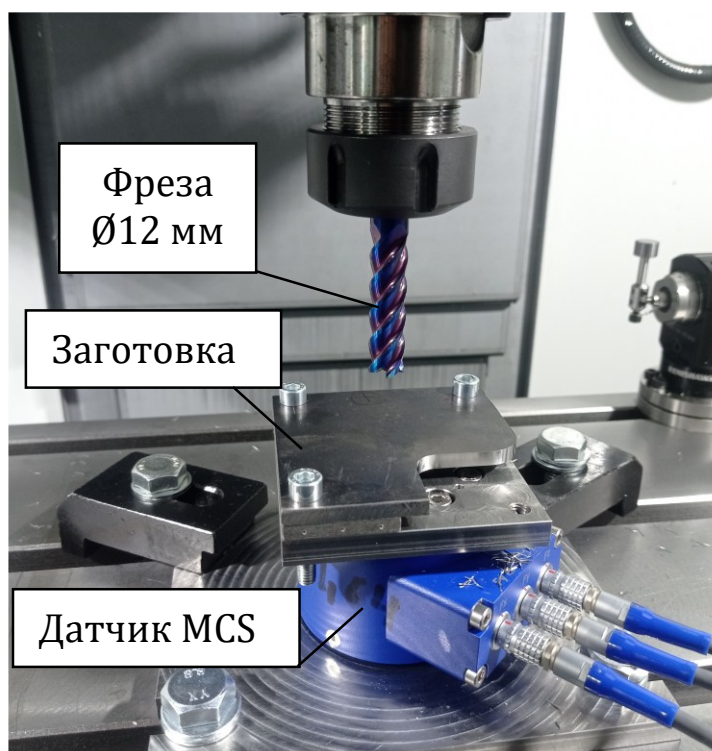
Заготовка та тензометричний датчик HBM MCS 10-005-3C на столі верстата з ЧПК [82]
